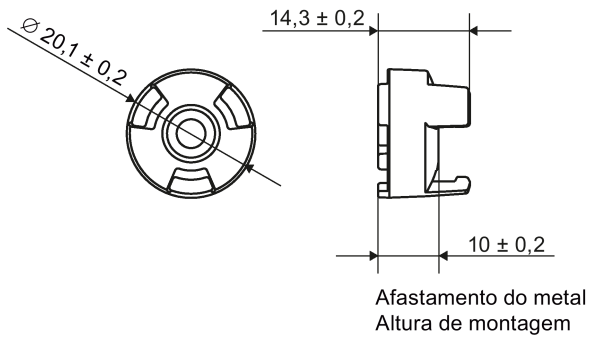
Desenho de dimensões do espaçador 6GT2690-0AG00
